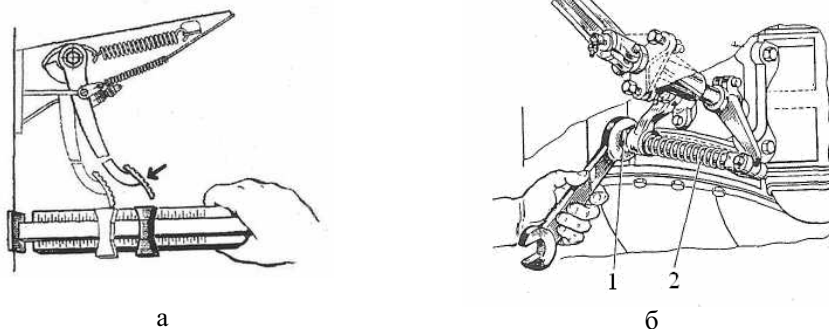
Схема проверки свободного хода педали сцепления (а) и его регулировка при механическом приводе (б):
